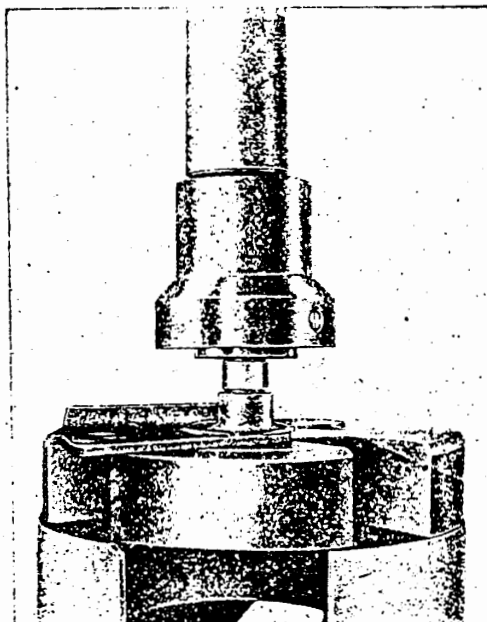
Kugellager mit Aufdrückdorn (Werkzeug Nr. 324.020-M 140) mit Handhebelpresse aufdrücken
